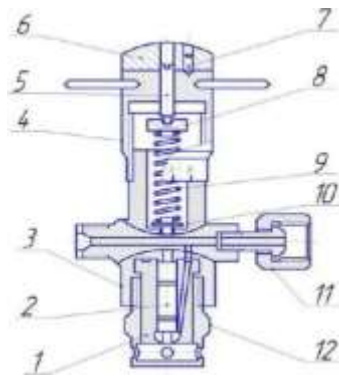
Максиметр: 1 - розпилювач; 2 - голка розпилювача; 3 - корпус; 4 – мікрометрична головка; 5 - гвинт встановлення; 6 - контргайка; 7 - стопорний гвинт; 8 - упор; 9 – пружина; 10 – натискний штифт; 11 – штуцер; 12 – гайка
